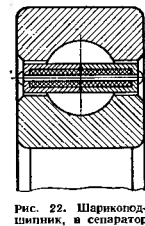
Шарикоподшипник, в сепаратор которого запрессована твердая смазка
